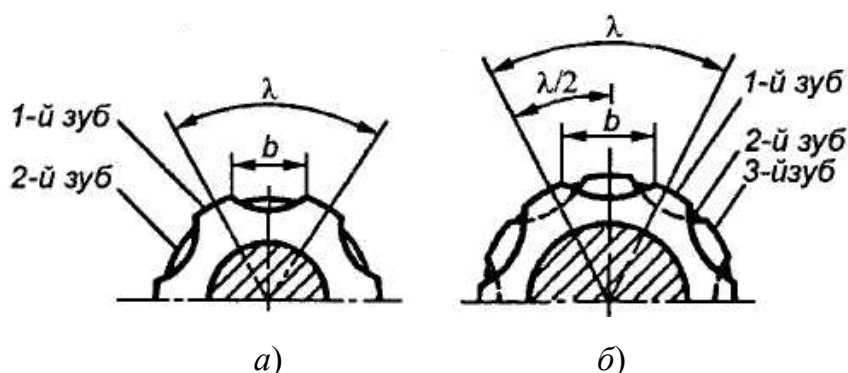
Схема расположения выкружек: а – группа из 2-х зубьев; б – из 3-х зубьев
